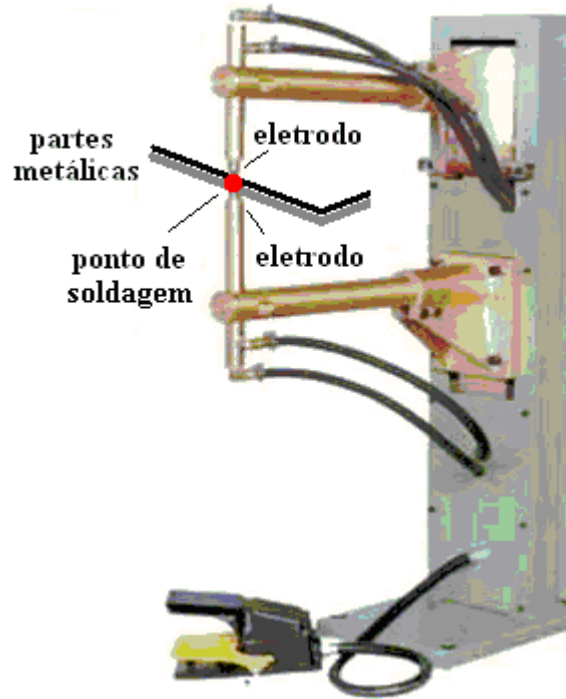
Desenho esquemático de uma máquina de solda a ponto resistiva
